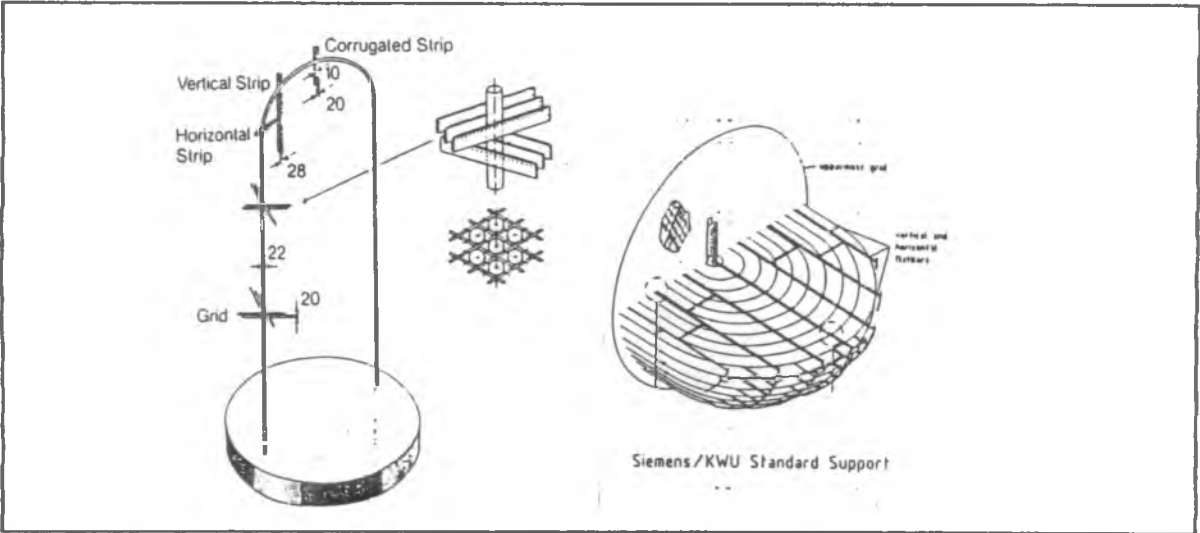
Estructura de apoyos en un GV Siemens/KWU [37]
